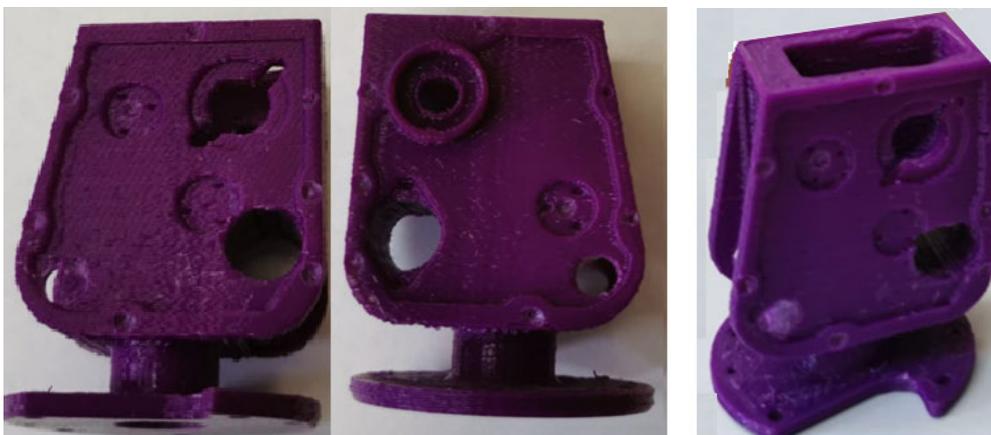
3D модель заготовки корпуса, изготовленная на 3д принтере
